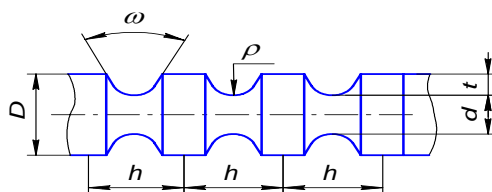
Рабочая часть образца для измерения остаточных напряжений
